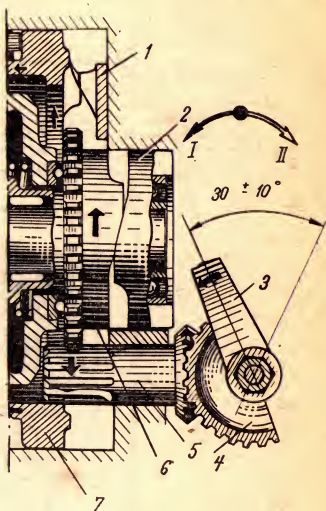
Механизм включения муфты сцепления пускового устройства дизеля А-01М: 1, 2 — неподвижные упоры; 3 — рычаг; 4 — шестерня; 5 — валик; 6, 7 — нажимные упоры
